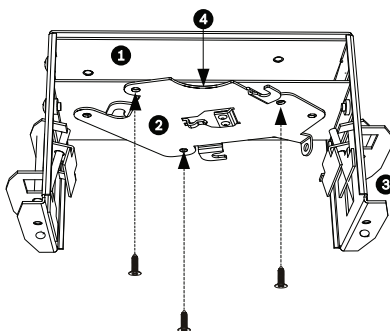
Fixar a placa de montagem ao suporte de montagem
